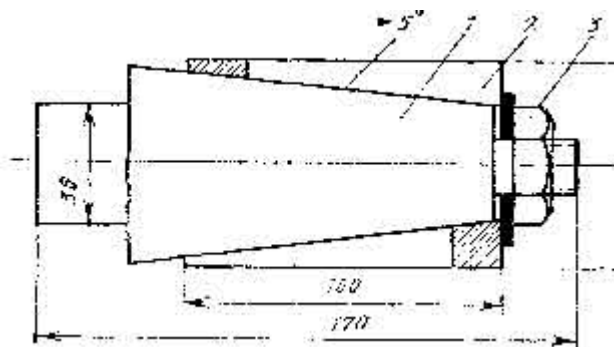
Притир для цилиндра двигателя мотоцикла ММВЗ: 1— корпус притира; 2—разрезная втулка; 3—гайка
